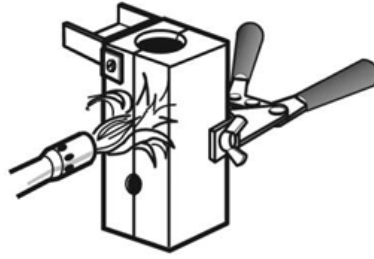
Antes de la primera soldadura, precalentar el molde (5 min aprox)
